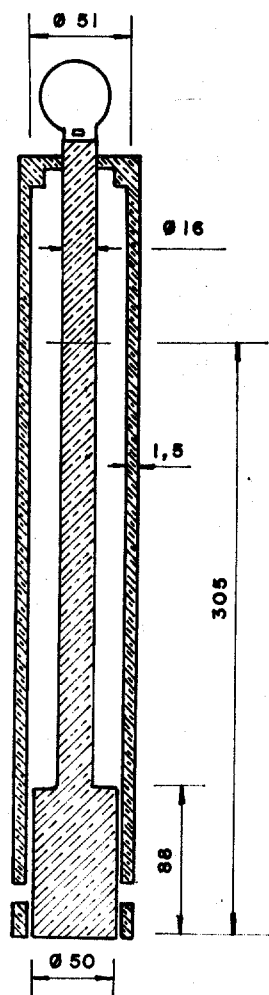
DIMENSÕES DO SOQUETE METÁLICO
